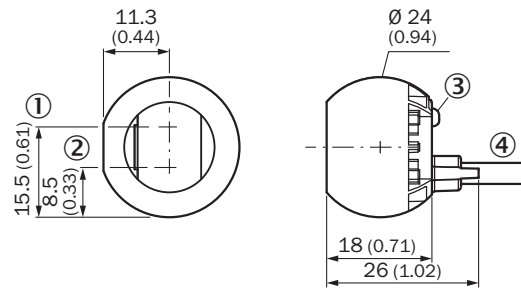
ZLx18-8xxxxx/ZLx18-Hxxxxx, cabo
